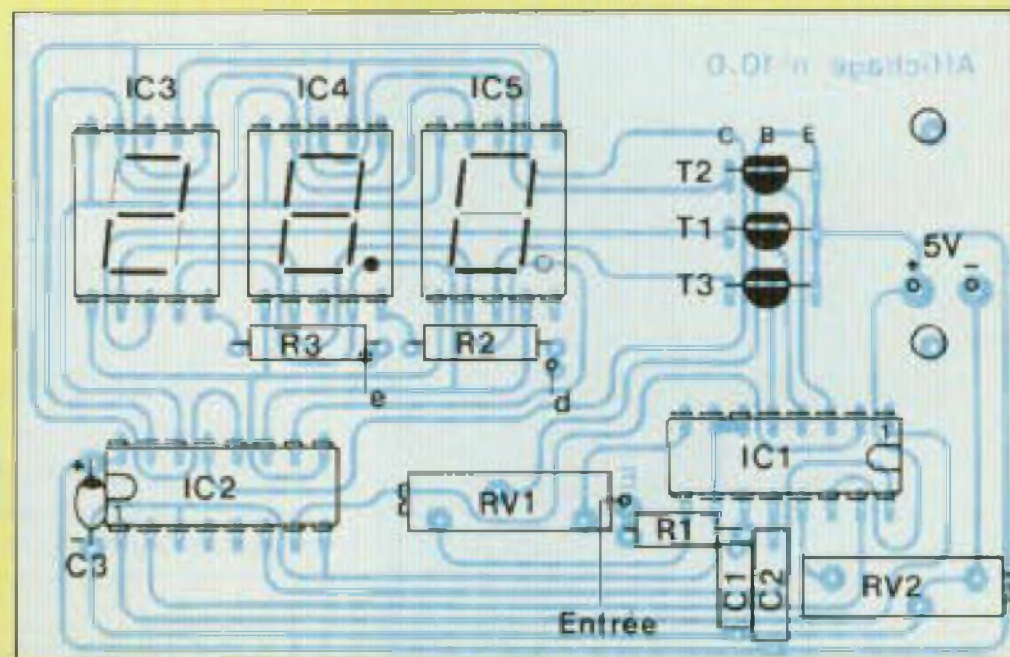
Un plan de câblage par contre qui n'autorise aucune erreur.
